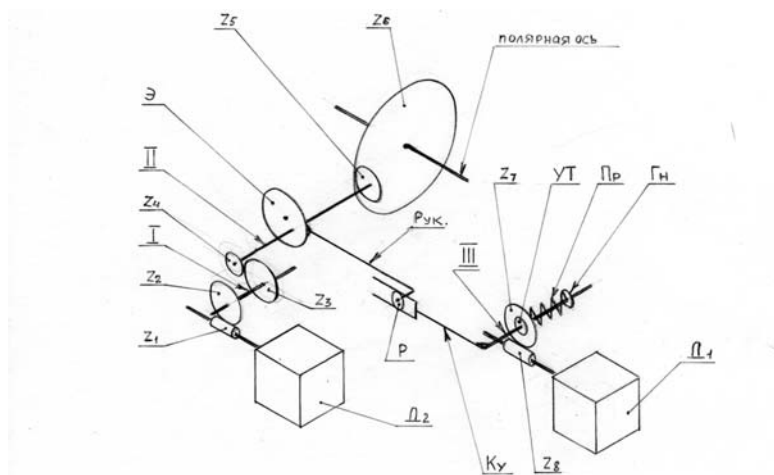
Кинематическая схема привода установочного поворота полярной оси.
